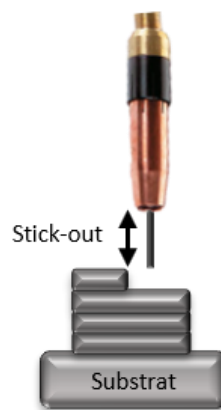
Schéma du stick-out et de la hauteur de la torche de soudage.
